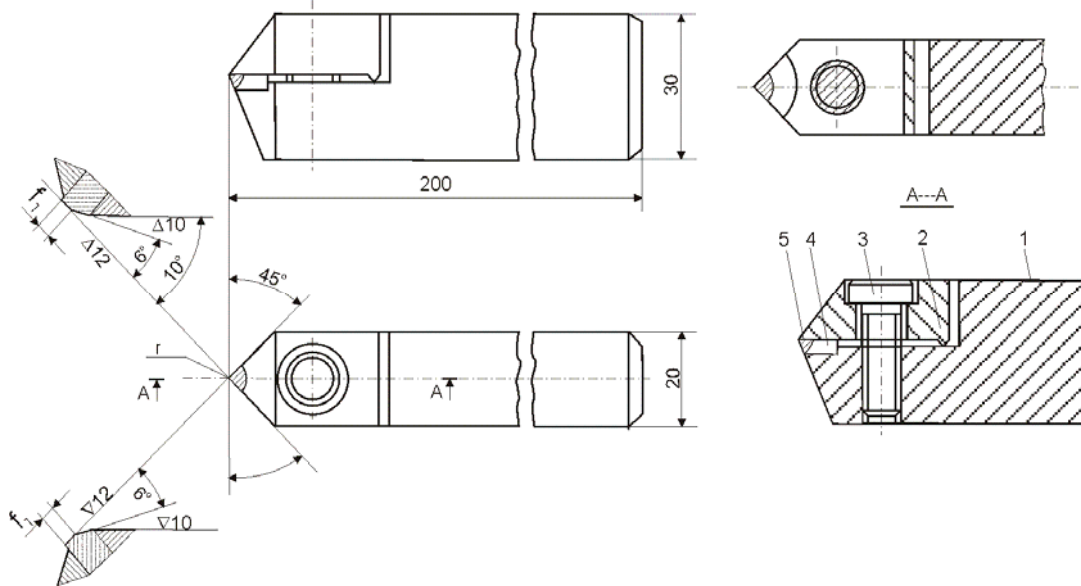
Збірний алмазний різець [1]: 1 – корпус; 2 – накладний притиск; 3 – гвинт; 4 – ріжуча вставка; 5 – алмазне зерно.
